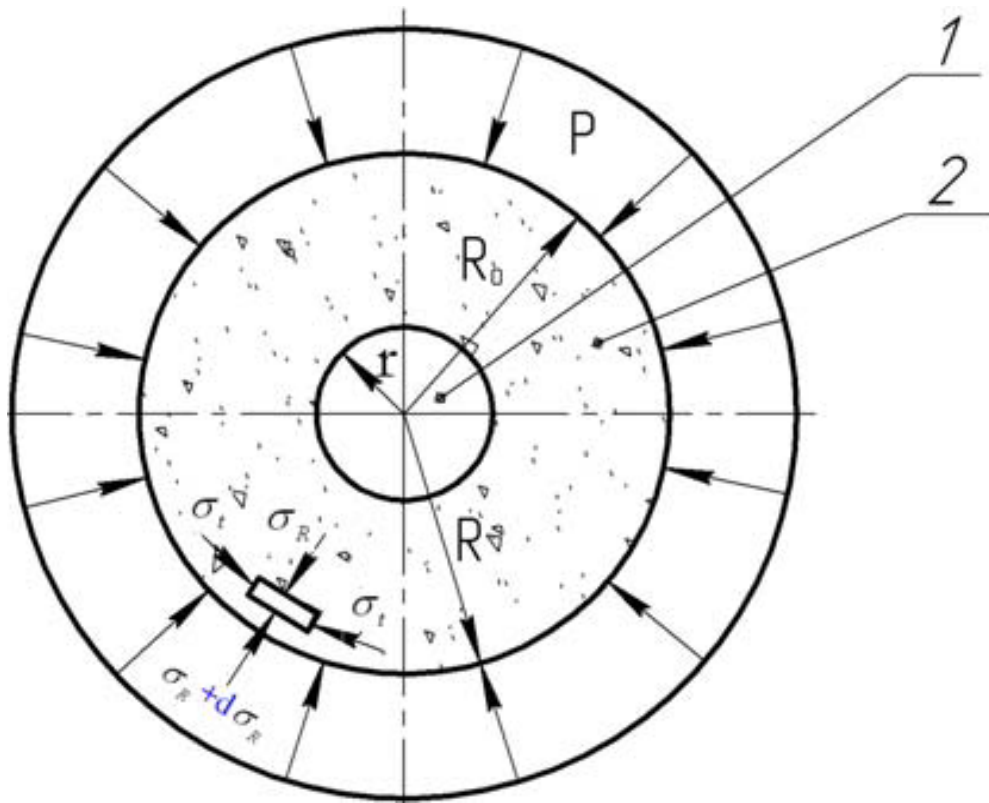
Схема для розрахунку тиску оброблювального середовища при обробці поверхонь тіл обертання: 1 – оброблювальна заготовка; 2 – оброблювальне середовище
